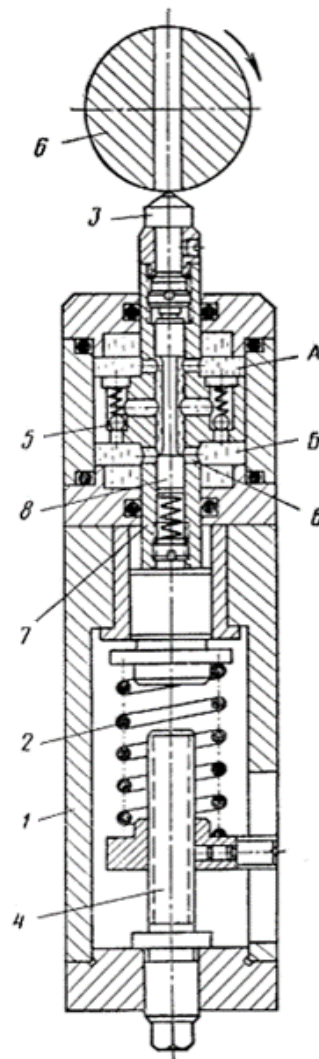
инструмент для алмазного выглаживания поверхностей детали вращения
